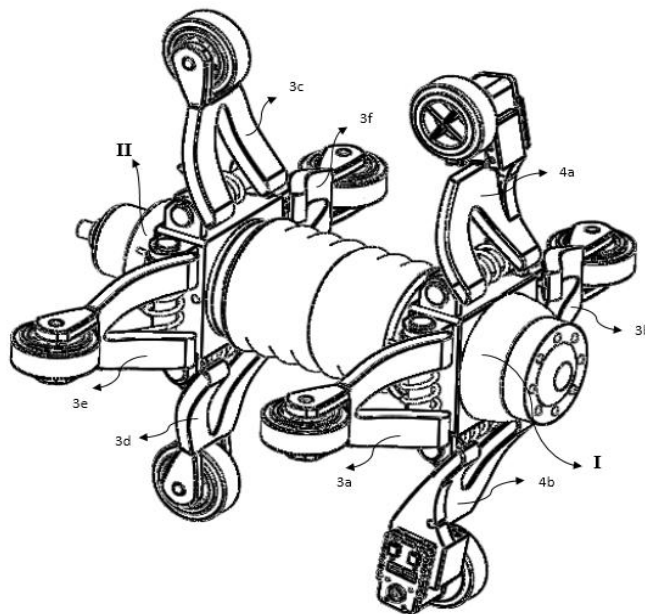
Diseño CAD del robot. Posición extremidades extendidas. (Vista isométrica)
